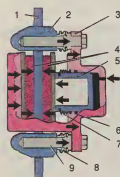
Схема работы "плавающей" скобы переднего тормоза: 1 — тормозной диск; 2 — основной; 3 — корпус скобы; 4 — тормозная колодка; 5 — поршень; 6 — уплотнительное кольцо; 7 — защитный чехол поршня; 8 — защитный чехол направляющего пальца; 9 — направляющий палец.
